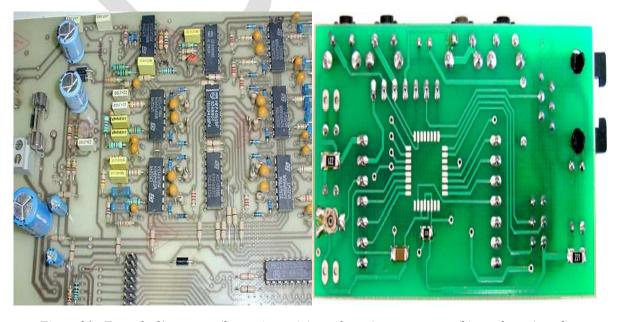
Exemple d'une carte électronique : (a) vue de coté composants et (b) vue de coté soudure.
